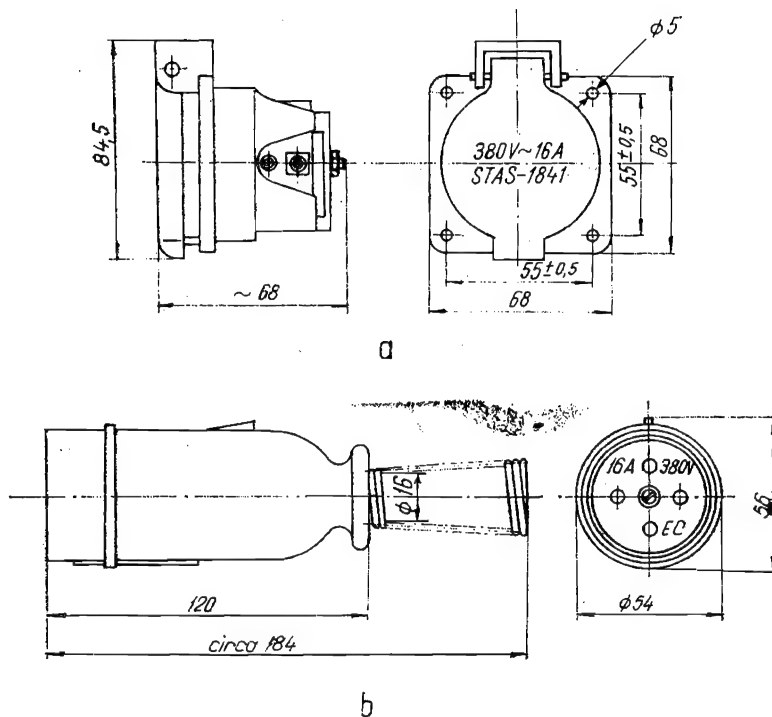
Priză și fișă tripolară de 16 A cu carcasă din silumin:
